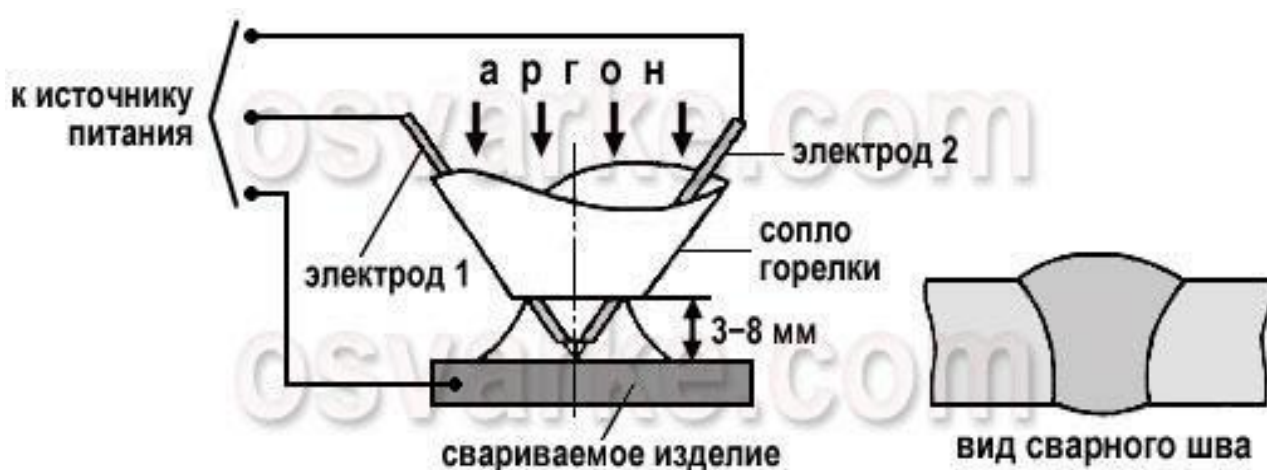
Схема выполнения сварки трёхфазной дугой
